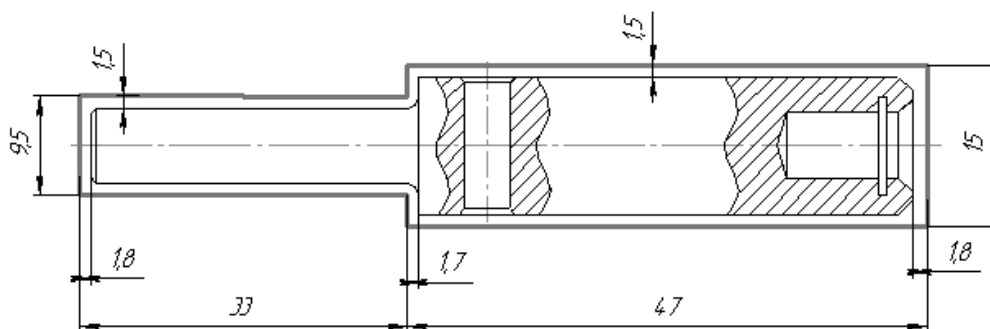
Ескіз заготовки – вилівка отриманого литтям в кокіль
